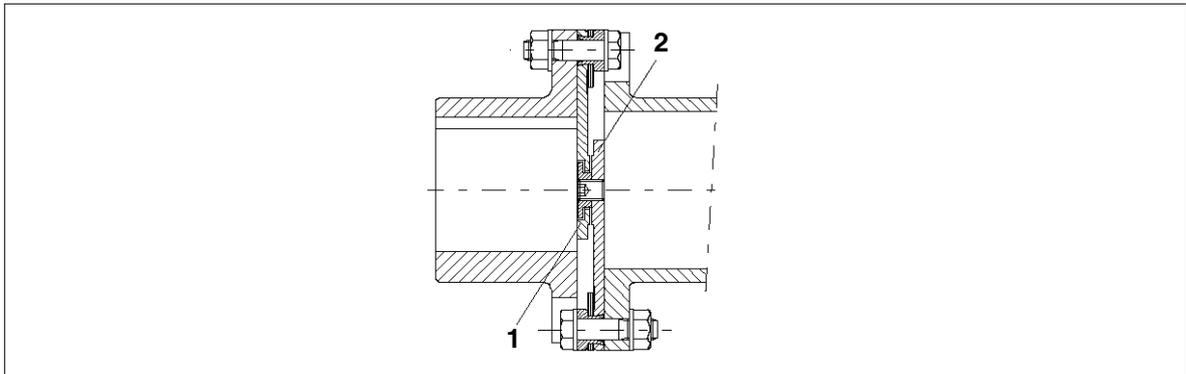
Montage der Lamellenpakete mit integrierter Axialspielbegrenzung
